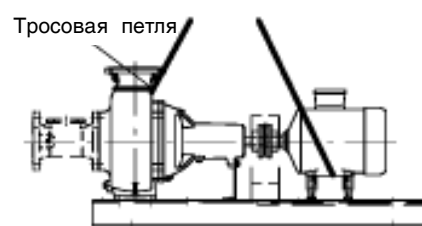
Транспортировка насосного агрегата в сборе (тип установки 3E)
